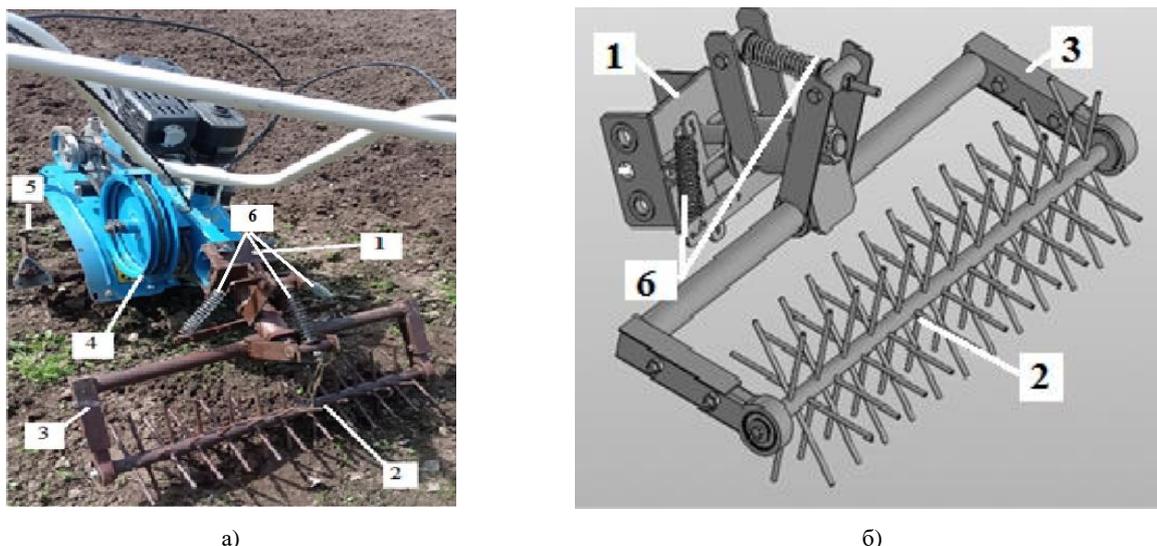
Пассивный игольчатый каток: а – общий вид агрегата; б – конструктивная схема прикатывающего катка: 1 – прицепное устройство, 2 – рабочий орган, 3 – рама катка, 4 – мотоблок, 5 – сегментная фреза, 6 – балансирующие пружины / Fig. 4. Passive needle roller: a – general view of the unit; b – design scheme of the rolling roller: 1 – trailer device, 2 – working body, 3 – roller frame, 4 – tillers, 5 – segment cutters, 6 – balancing springs
